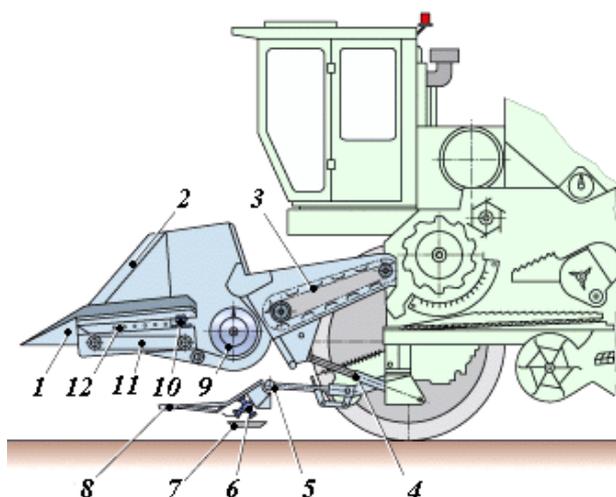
Приспособление ПСП-10 для уборки подсолнечника:
